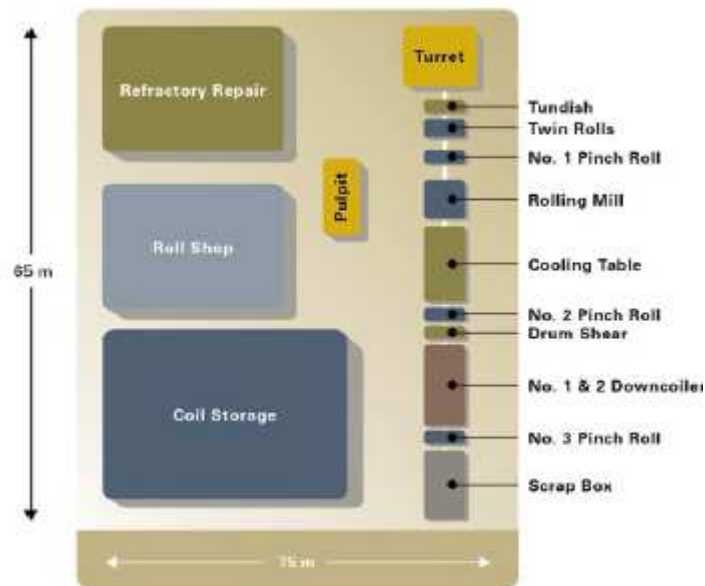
Esquema de la distribución en planta de una planta de colada continua mediante solidificación rápida.
